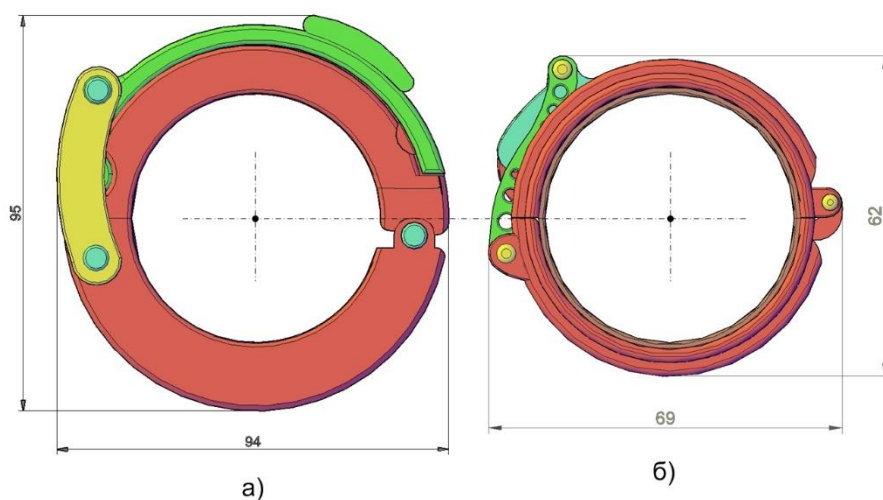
Зажим в закрытом положении (главный вид): а – старого образца; б – нового образца
